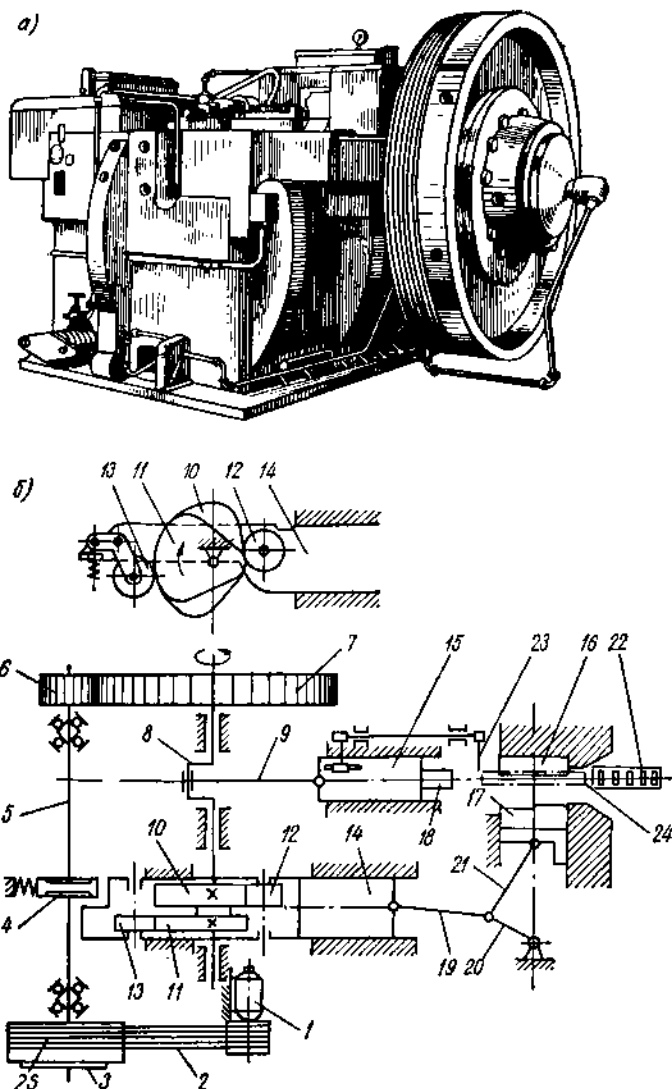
Общий вид и кинематическая схема горизонтально-ковочной машины
